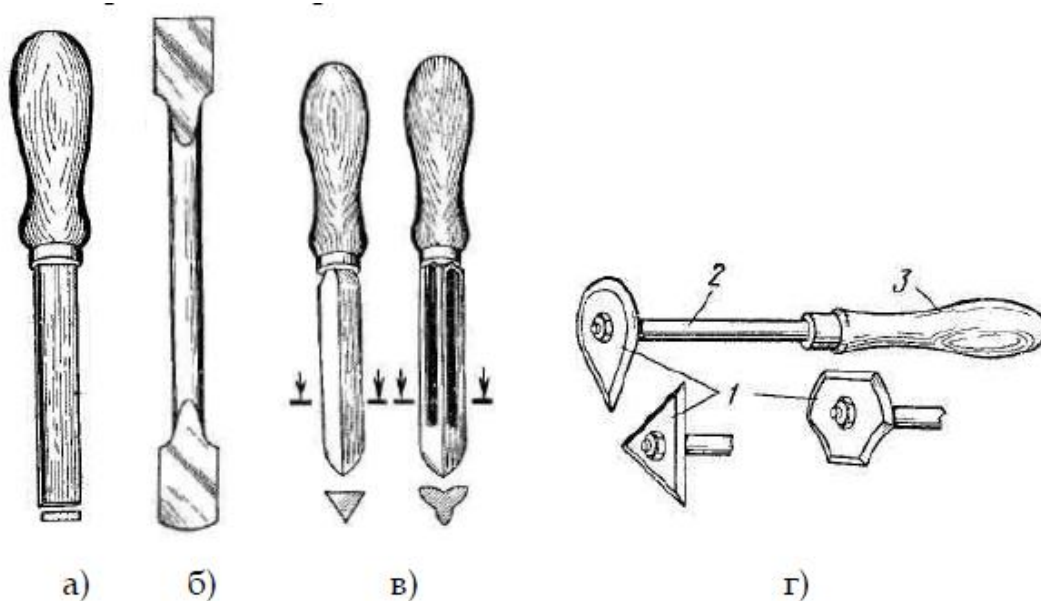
Шабери: а – плоский однобічний; б – плоский двобічний; в – тригранний; г – фасонний: 1 – набір пластин; 2 – стержень; 3 – ручка
